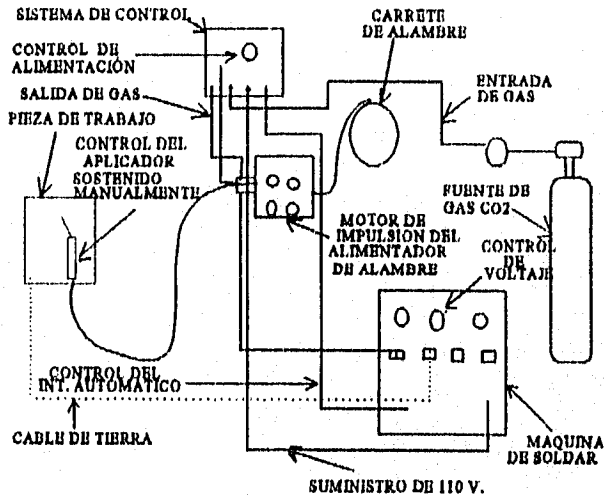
Partes componentes de un sistema de soldadura Mig-Well.
